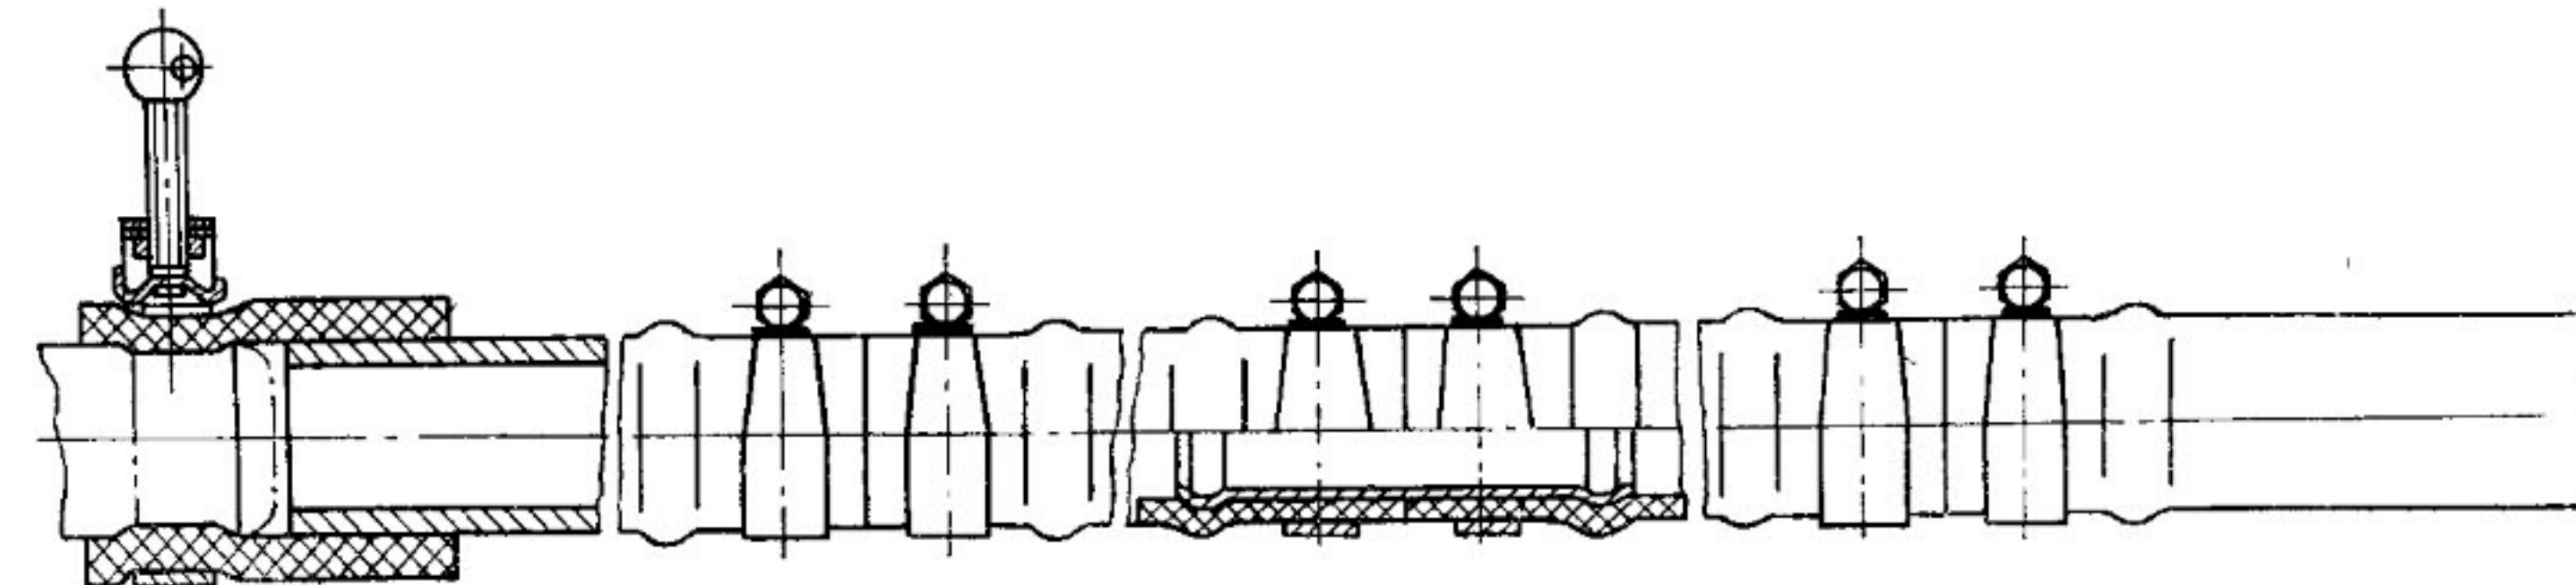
Шланг слива масла из хвостового и промежуточного редукторов
